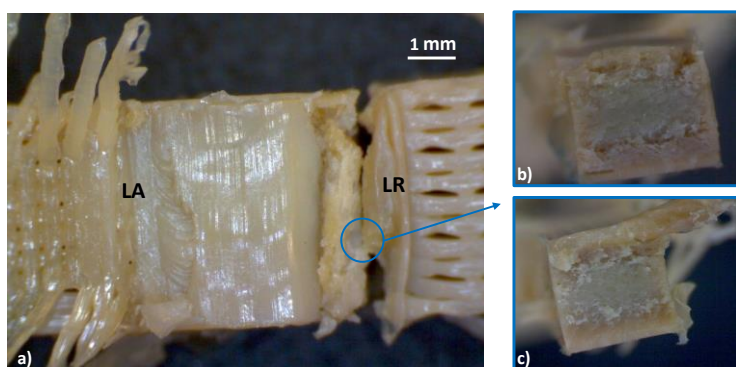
Macrografia do provete após Ensaio 3: a) Superfície superior do provete, b) Superfície de fratura do cordão de soldadura do LR, c) Superfície de fratura da interface do material base com o LR.
